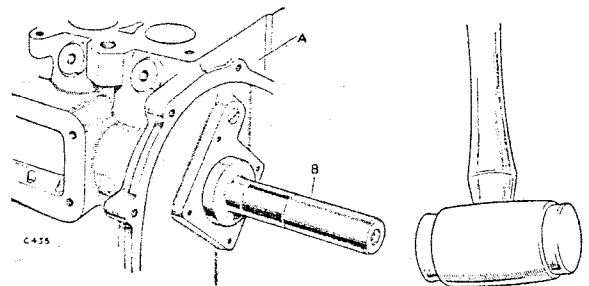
Desmontaje del cojinete exterior del árbol de levas.
